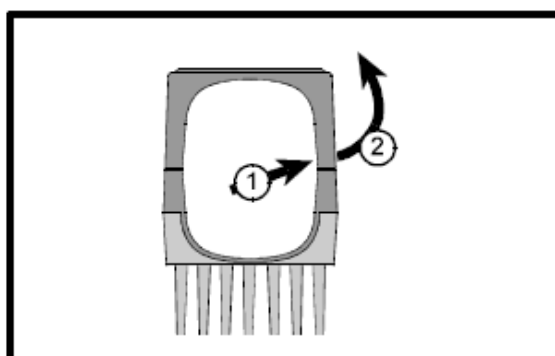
Вид снизу, показывающий как клеммная крышка снимается с Привода
